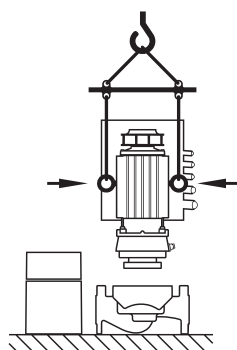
Transportul ansamblului motor cu rotor hidraulic
